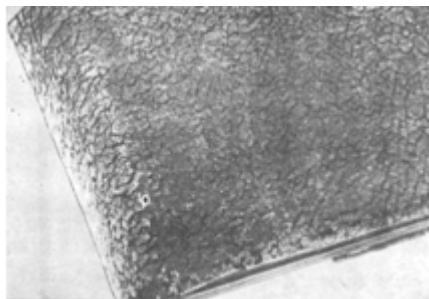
Внешний вид заготовки с чешуйчатостью
